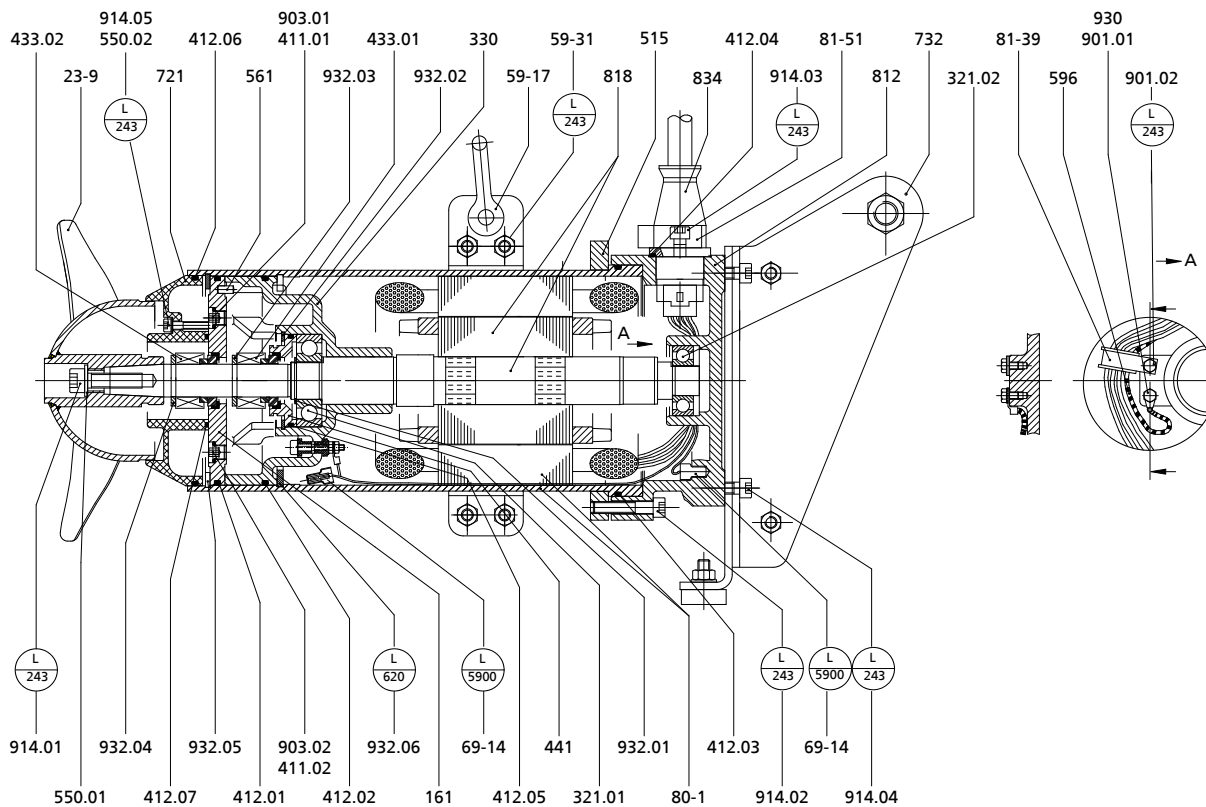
Чертеж общего вида Amamix 200, материал корпуса двигателя – высококачественная сталь
